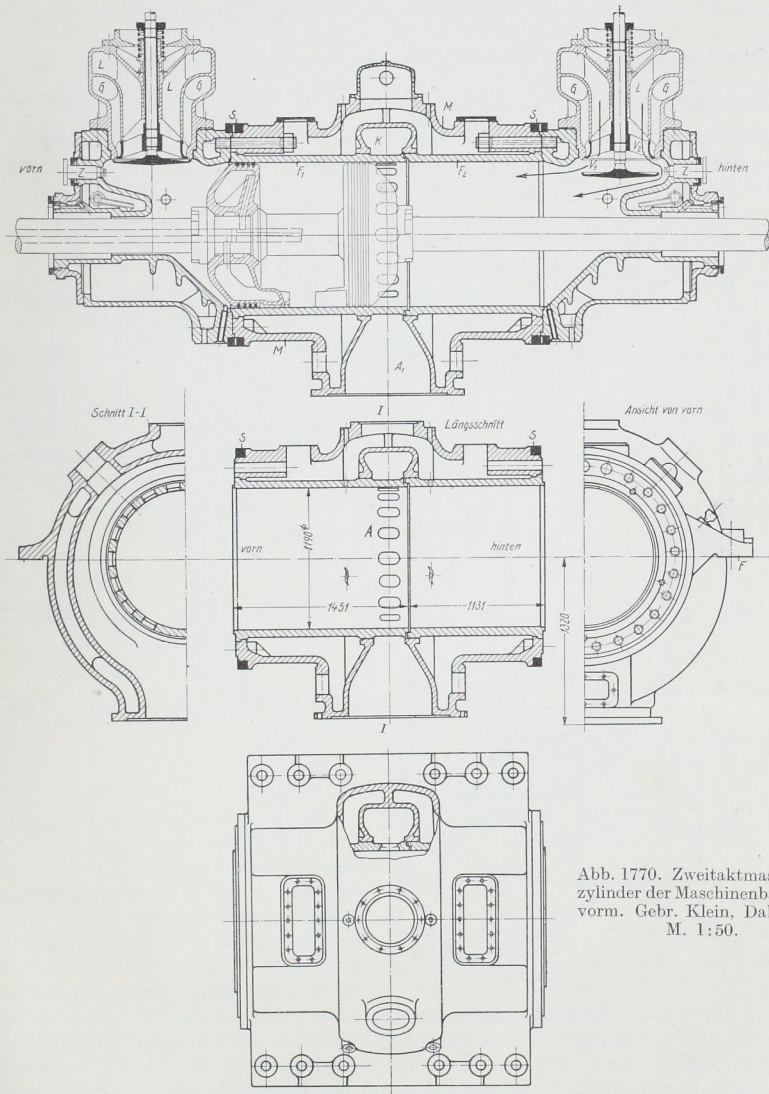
Zweitaktmaschinenzylinder der Maschinenbau A.G., vorm. Gebr. Klein, Dahlbruch. M. 1:50.
